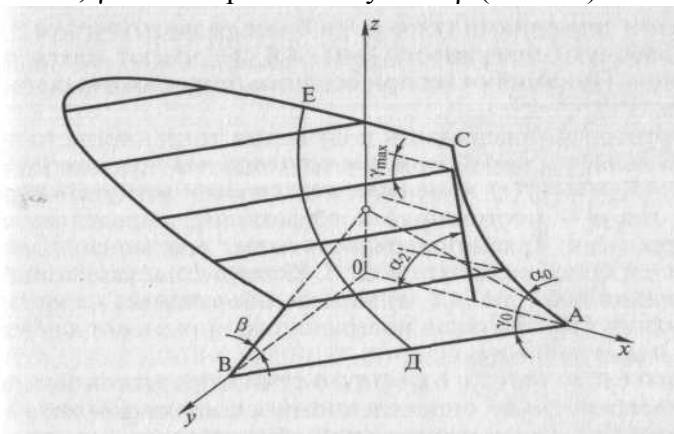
Схема образования рабочей поверхности корпуса плуга.
